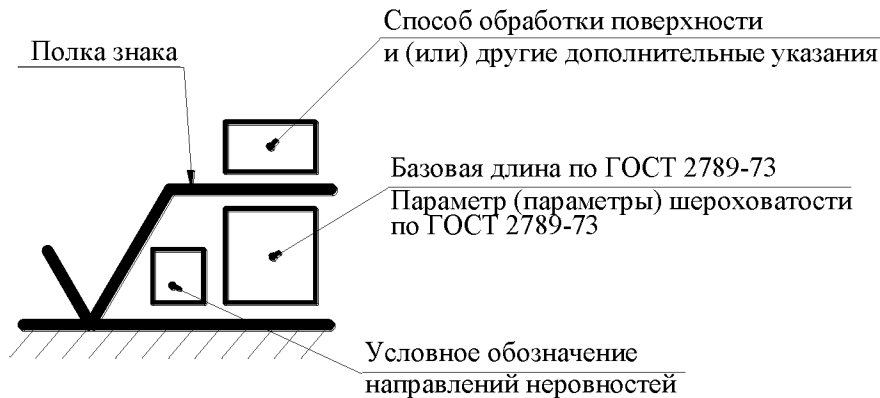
Обозначение шероховатости поверхности на чертежах
